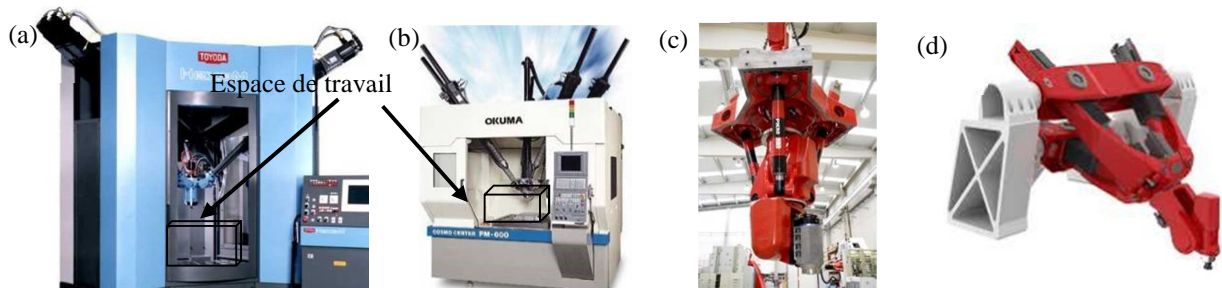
Machines-outils parallèles d'usinage : HexaM de TOYODA (a) et cosmo center PM-600 de OKUMA(b), Architecture hybride d'usinage: PKM Tricept(c), Exechon(d)
